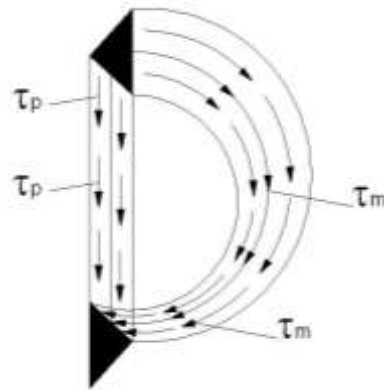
Diagrama cuerpo libre del cordón de soldadura
